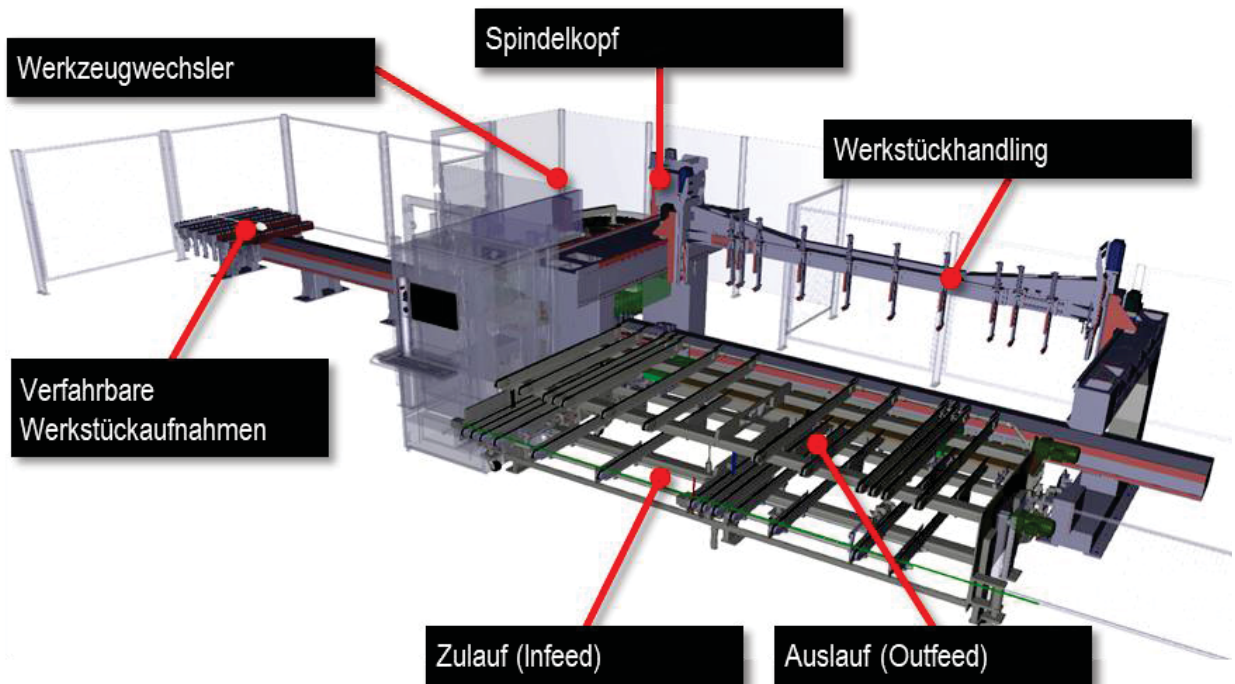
Beispielmaschine aus virtuellen Baugruppen, Werkzeugverwaltung und Materialflusselemente
